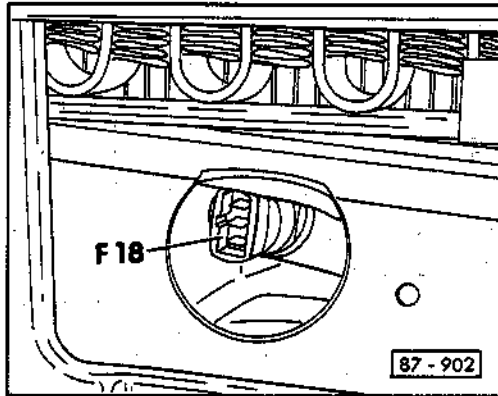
Thermostalter für Lüfter für Kühlmittel – F 18
